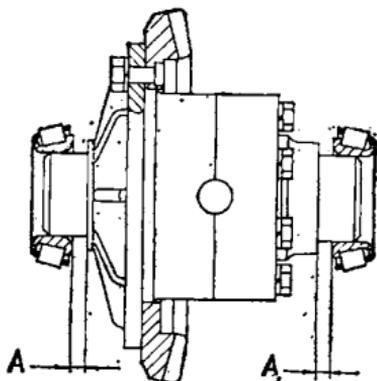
Зазоры A и A_1 между торцами подшипников и коробки сателлитов
